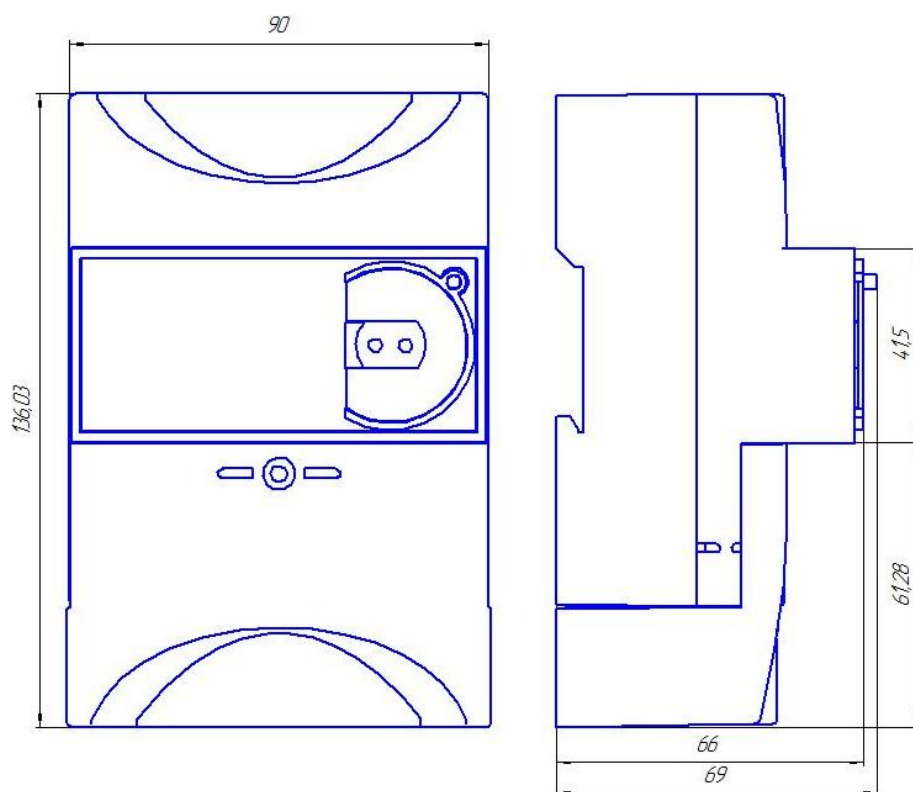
Габаритный чертеж и установочные размеры счетчиков МАЯК 101АТД с крышкой МНЯК.731323.008.
